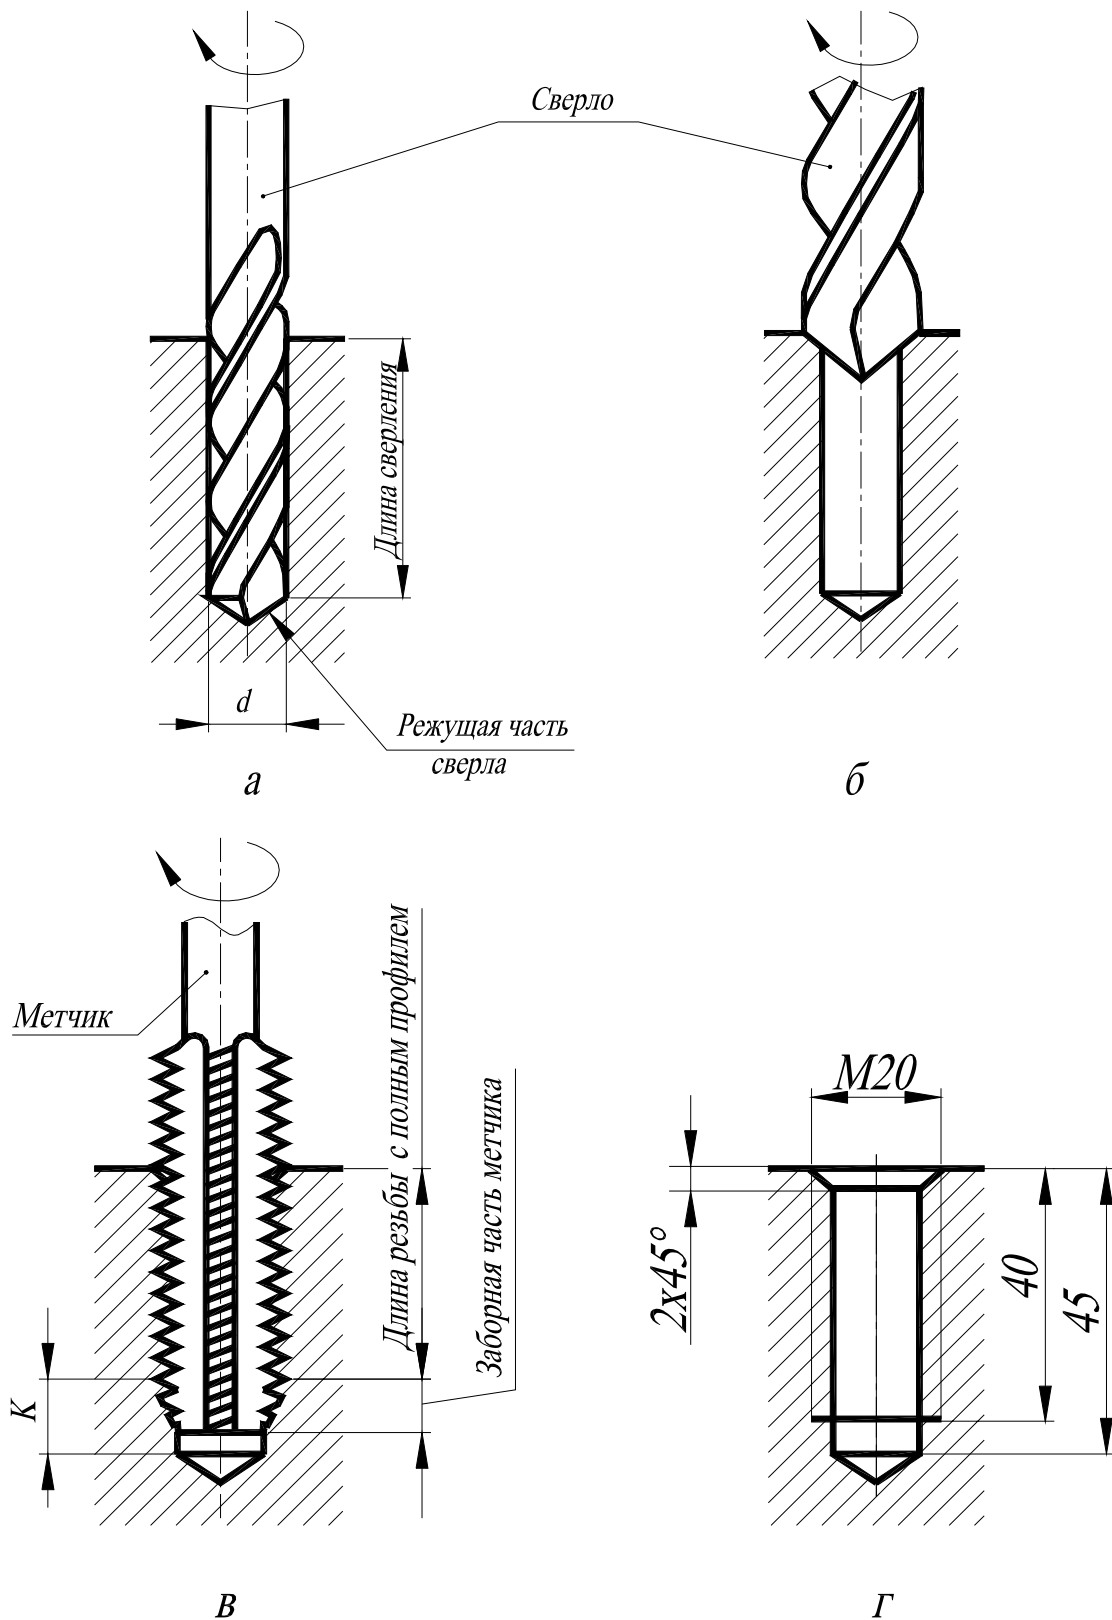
Этапы получения глухого резьбового отверстия: а – сверление цилиндрического отверстия; б – снятие фаски; в – нарезание резьбы метчиками; г – состав размеров на чертеже
